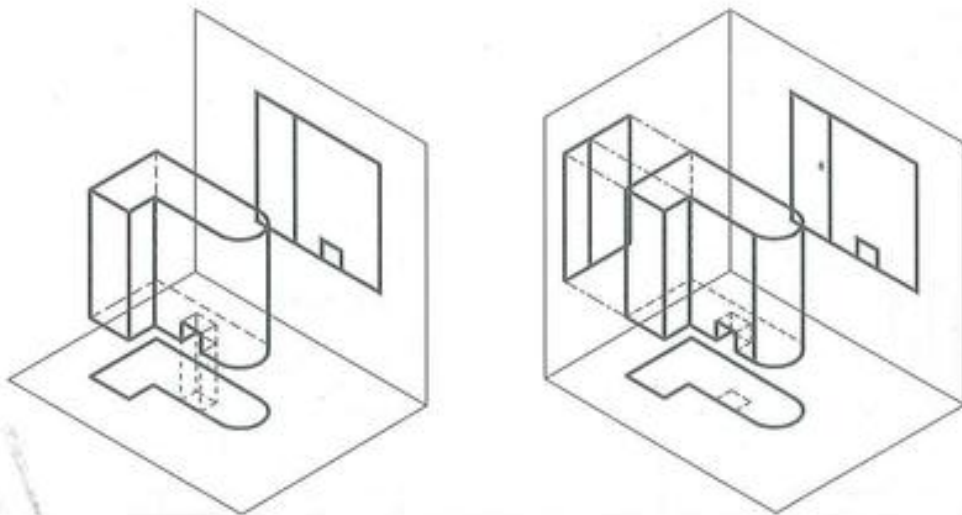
Proyección sobre el plano inferior de la pieza y sobre el plano lateral izquierdo.
